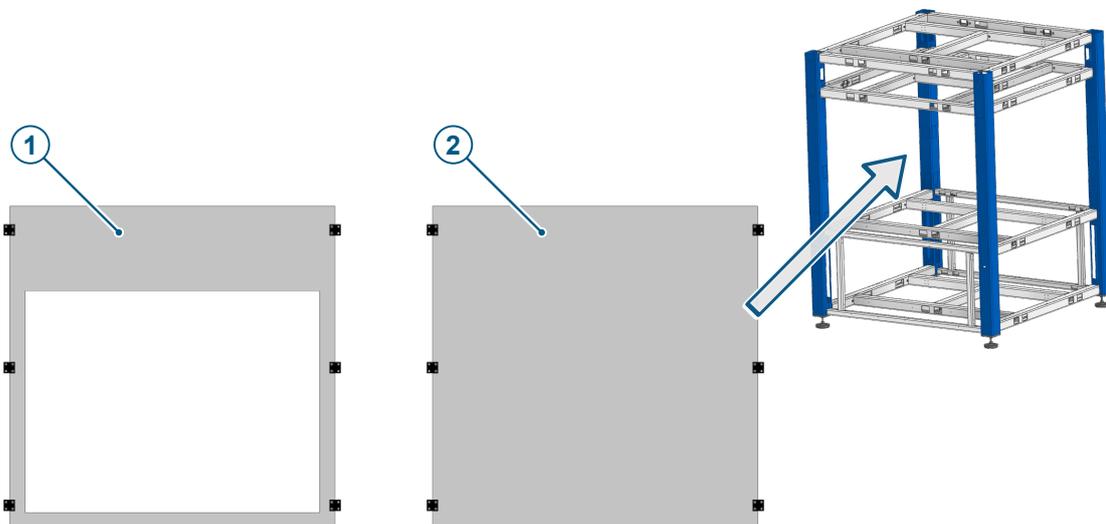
Optionen Einschraubwand mit Fenster und Einschraubwand geschlossen
